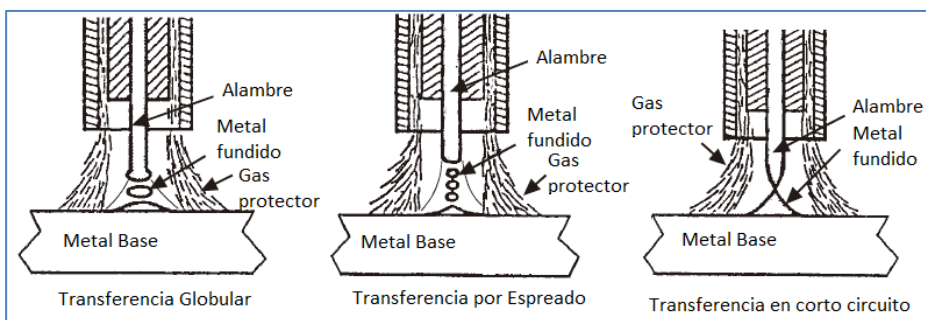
1 Proceso de soldadura por arco metalico con gas de proteccion (3)
